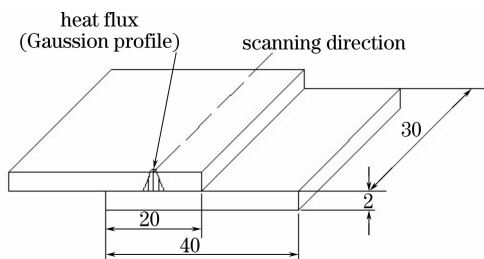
PVC 焊接试验焊接形式及样品尺寸
